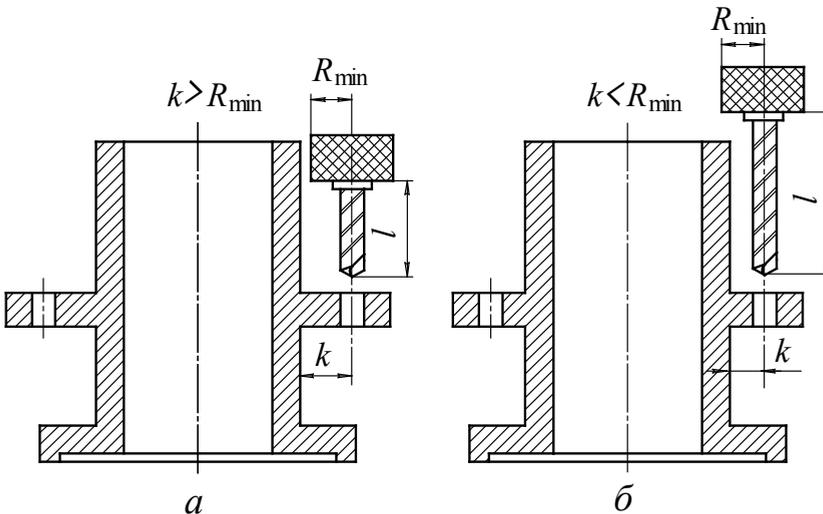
Конструкция корпусных деталей с отверстиями на фланце:
